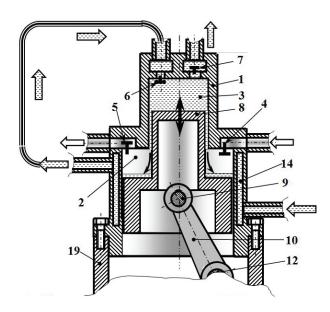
Цилиндропоршневая группа ГЭМОД с тронковым поршнем и верхним расположением жидкостной рабочей полости (обозначения см. на рис. 5)
